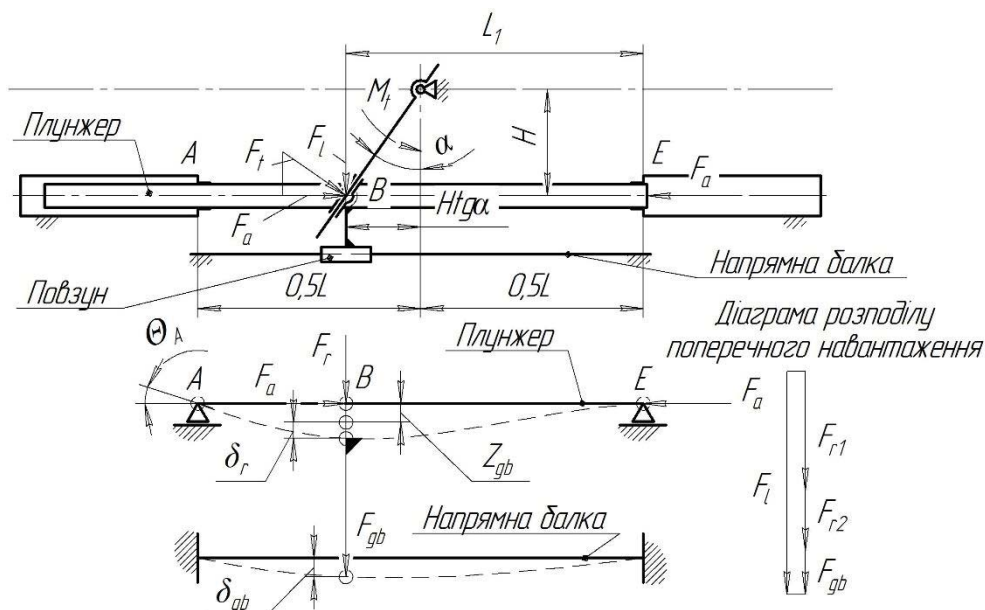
Розрахункова схема механізму рульової машини Р-18
